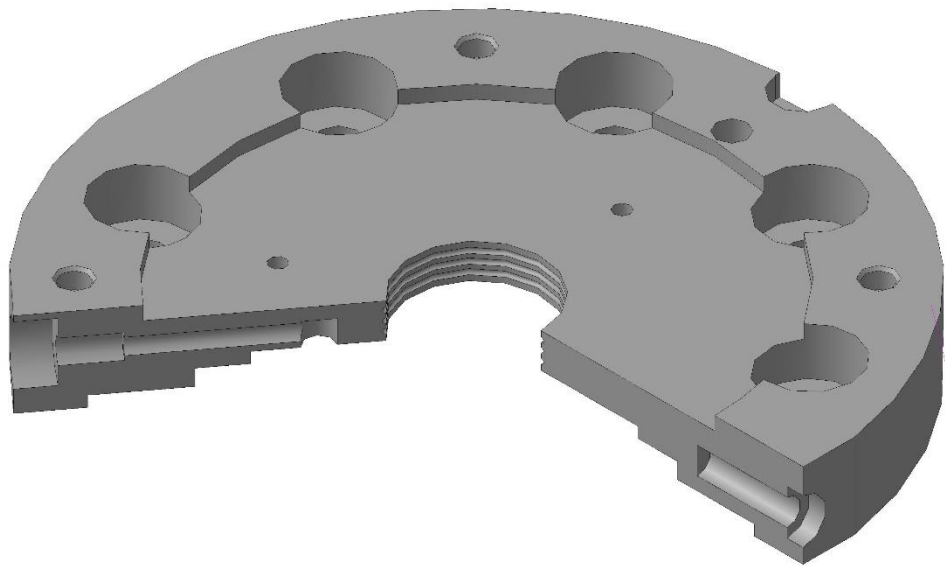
Твердотельная модель детали «Крышка», $m = 7,580$ кг
